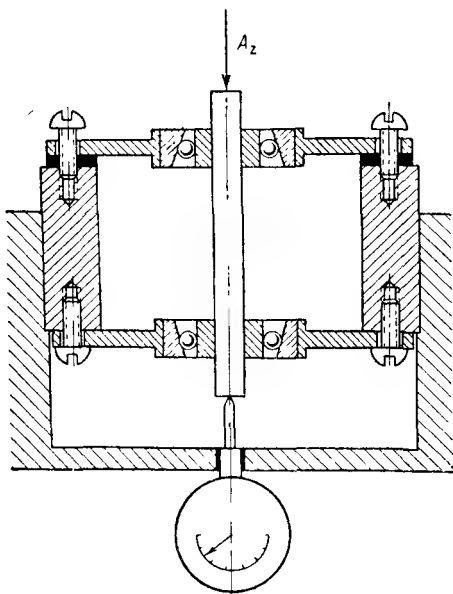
Схема установки и контроля предварительной осевой нагрузки на подшипники
